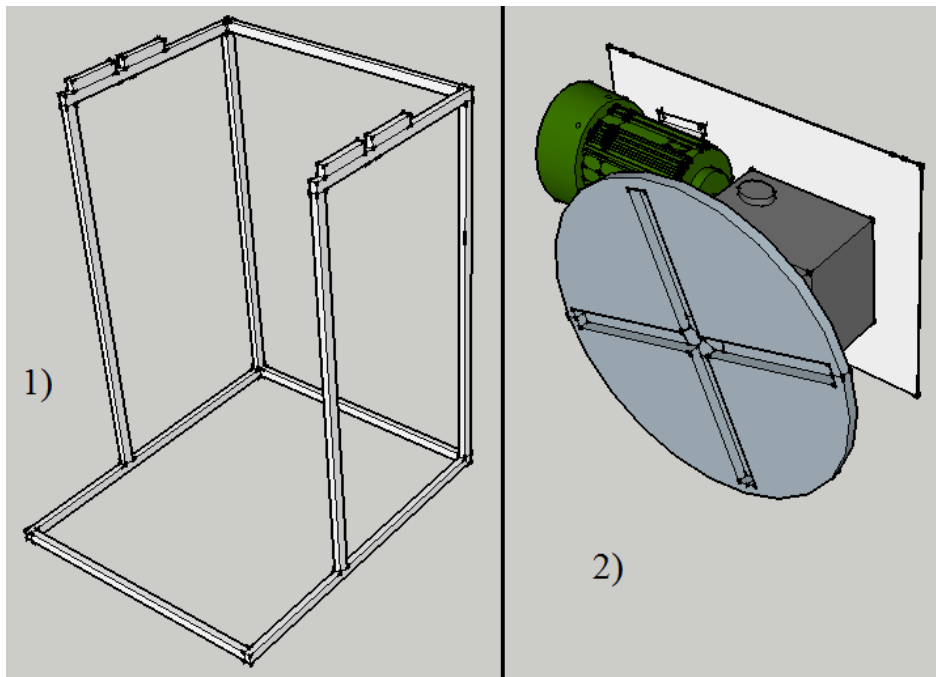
e 3.7. 1) Sistema de Giro da Tocha; 2) Base de Fixação.
